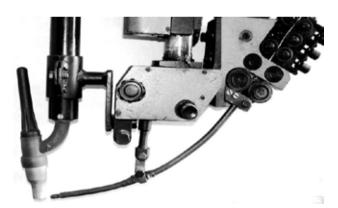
Внешний вид горелки для сварки неплавящимся электродом фирмы «Fronius»
